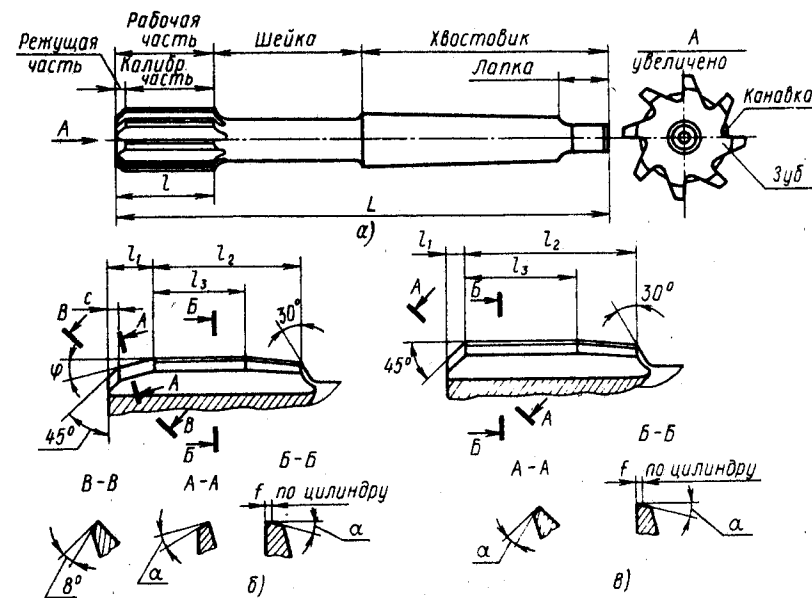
Конструктивные элементы (а) и элементы режущей части (б, в) развертки
